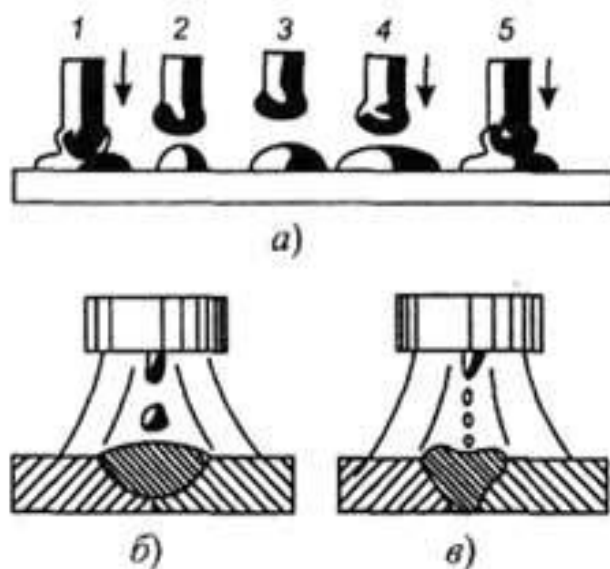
Основные формы расплавления и переноса электродного металла: а – короткими замыканиями; б – капельный; в – струйный
